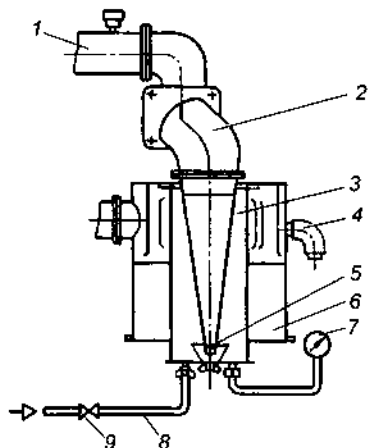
Схема проверки герметичности системы питания воздухом двигателей автомобилей КамАЗ, КамАЗ-5410, КамАЗ-4310 и КамАЗ-5511: 1 — впускной коллектор двигателя; 2 — проверяемый участок впускного тракта; 3 — заглушка (приспособление для проверки герметичности впускного тракта); 4 — трубопровод к эжектору отсоса пыли; 5 — дымообразующий материал; 6 — воздушный фильтр; 7 — манометр; 8 — шланг подвода сжатого воздуха; 9 — устройство для регулирования давления воздуха
